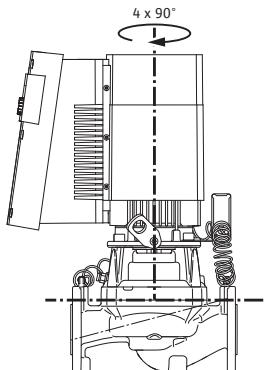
Допустимі монтажні положення з вертикальним розташуванням вала двигуна
